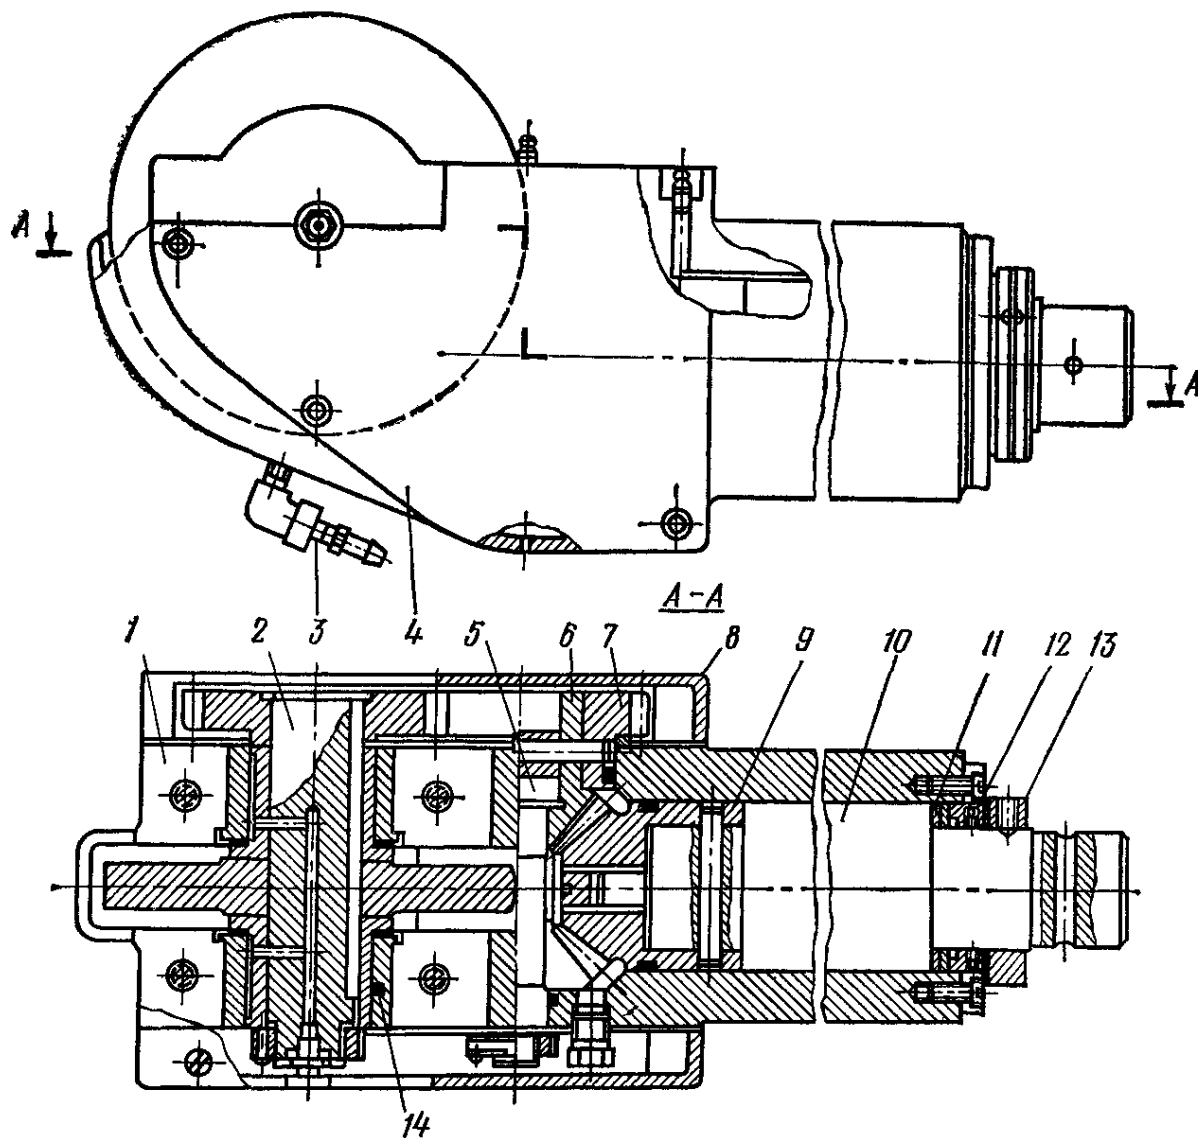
Электродное устройство с ведущим электродом для продольной сварки: 1 — корпус, 2 — токоведущий вал с роликом, 3 — ниппель водяного охлаждения, 4, 8 — щелка, 5 — вал, 6, 9 — коническое зубчатое колесо, 7 — цилиндрическое зубчатое колесо, 10 — карданный вал, 11 — шайба, 12 — сальник, 13 — стопорное кольцо, 14 — токоведущая втулка
